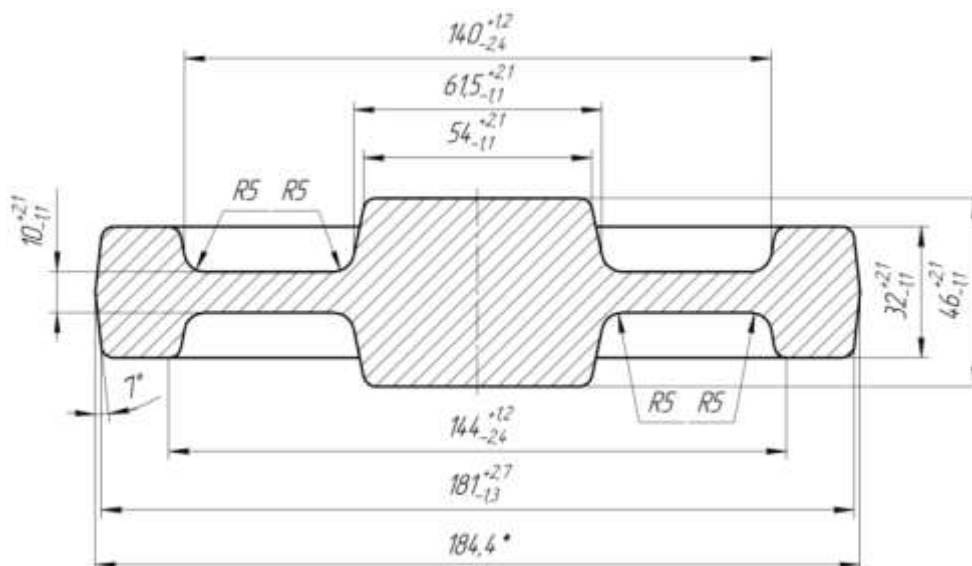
Чертеж поковки шестерни 12.37.118
